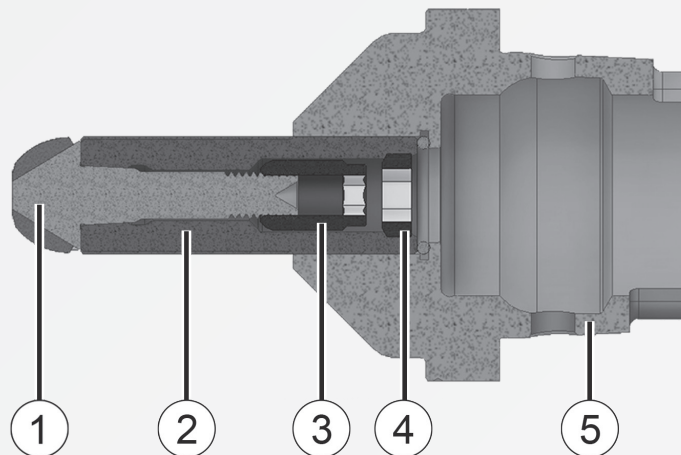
Schnittdarstellung Outer Race Werkzeuge
